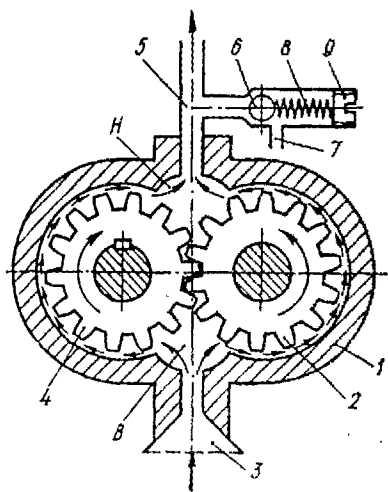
Схема действия насоса системы смазки: 1 – корпус; 2 и 4 – ведомая и ведущая шестерни; 3 – маслозаборник; 5 – канал нагнетания; 6, 8 и 9 – запорный шарик; пружина и регулировочный винт предохранительного клапана; 7 – отверстие для перепуска масла
